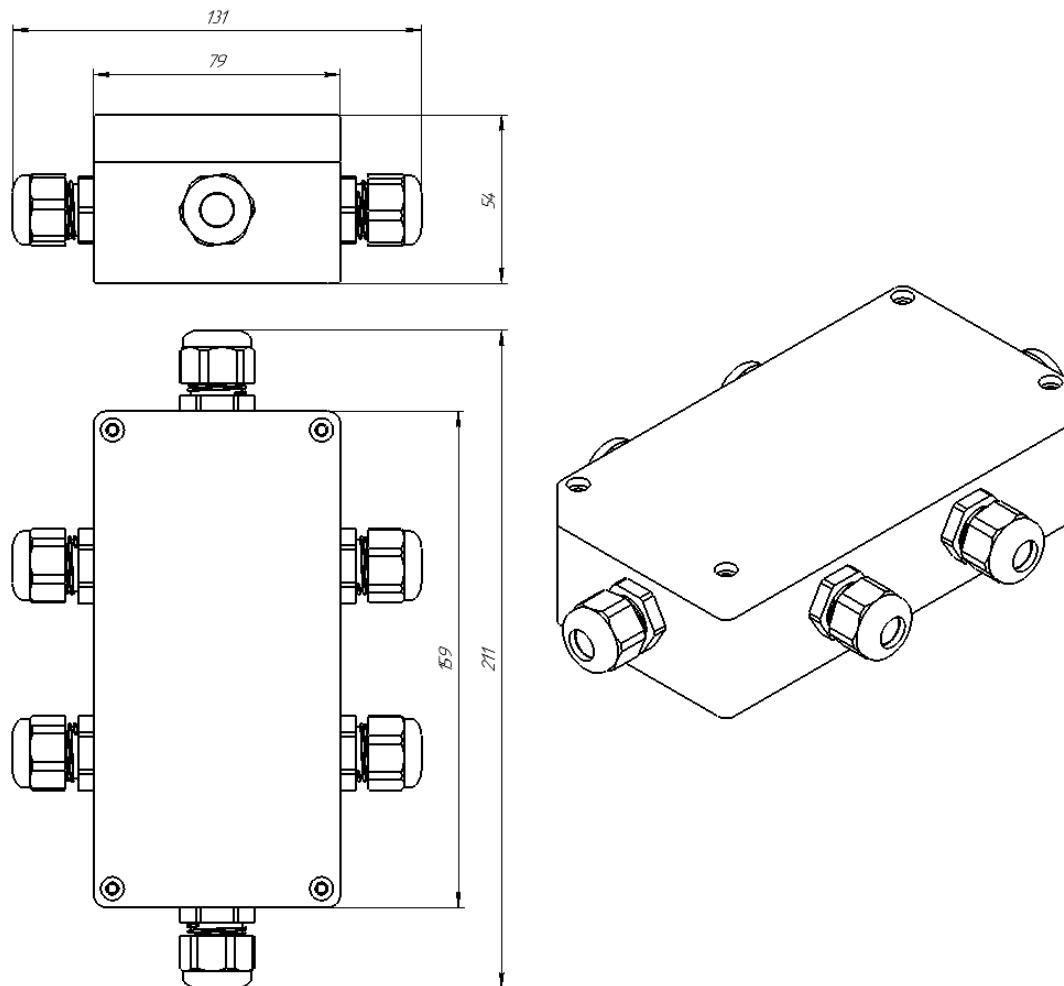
Габаритные и установочные размеры ПР-6У IP65
